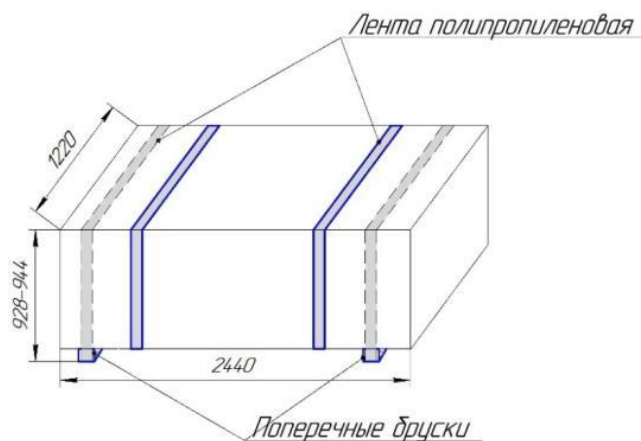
Вид транспортного пакета размером 2440x1220 мм
